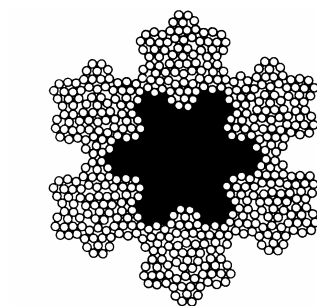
Secțiune transversală printr-un cablu triplu
